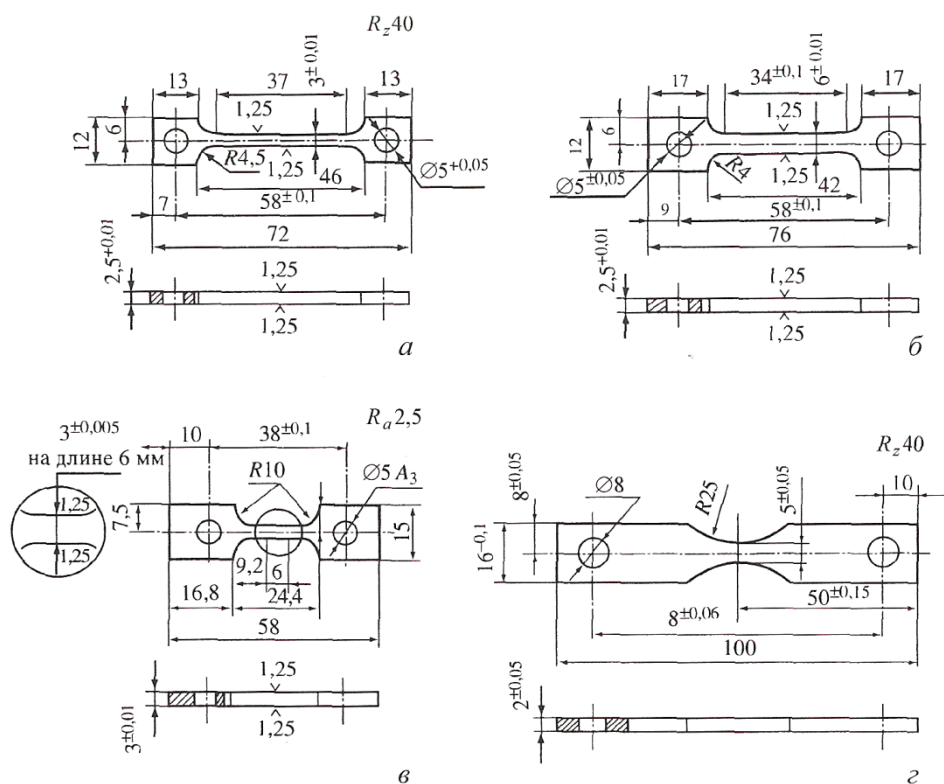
Образцы для проведения испытаний четырех типов [274]
